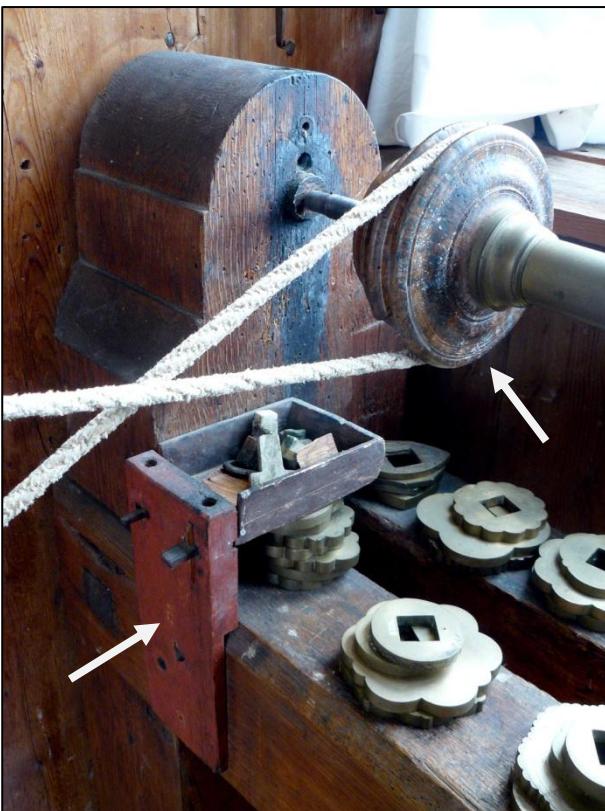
Spindeldokken nr. 3923 (Carl Gustaf Wrangel)
